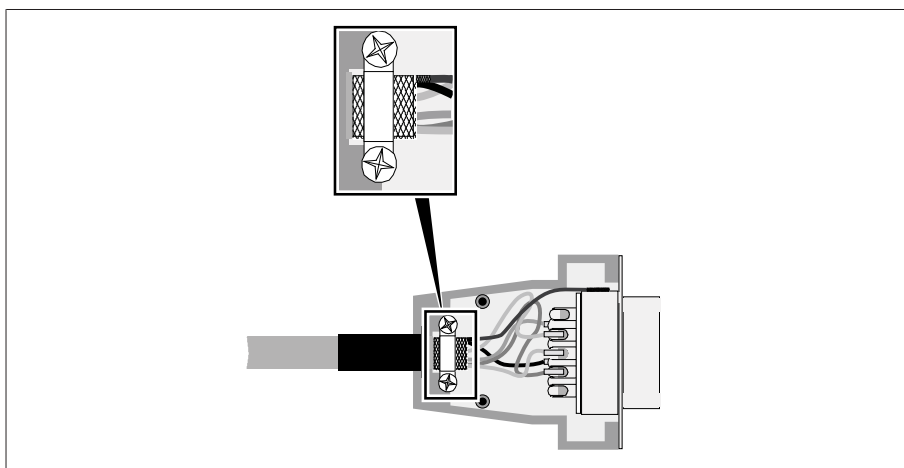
Exemplo de uma blindagem soldada à caixa do conector
